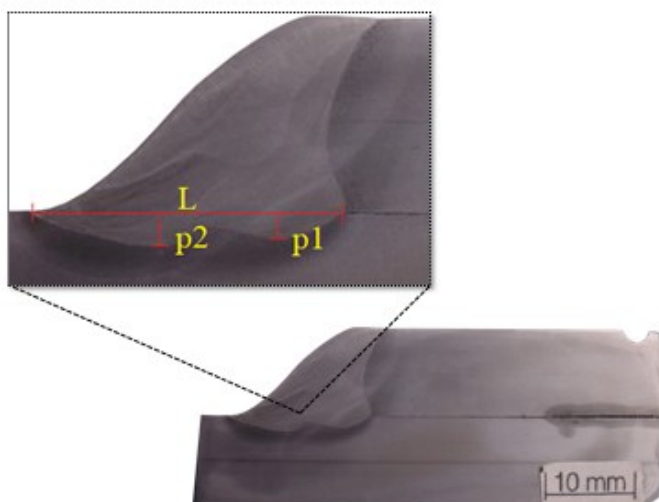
Macrografias em detalhe das juntas soldadas
